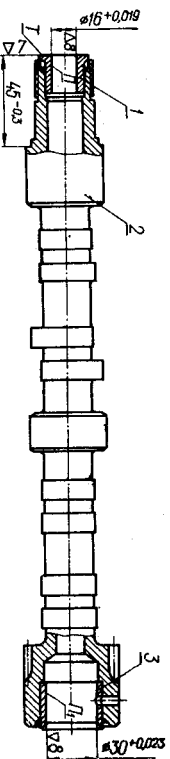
Вал распределительный в сборе: 1 — втулка балансирного вала; 2 — вал распределительный; 3 — втулка подшипника.
